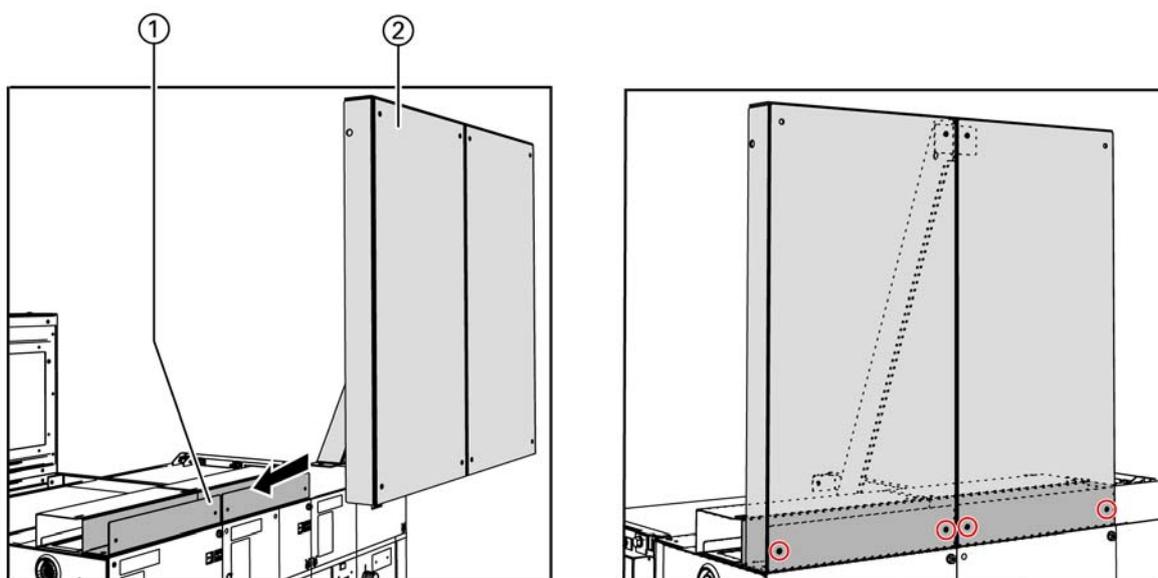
Крепление передних заглушек (2) на угловых кронштейнах (1)
